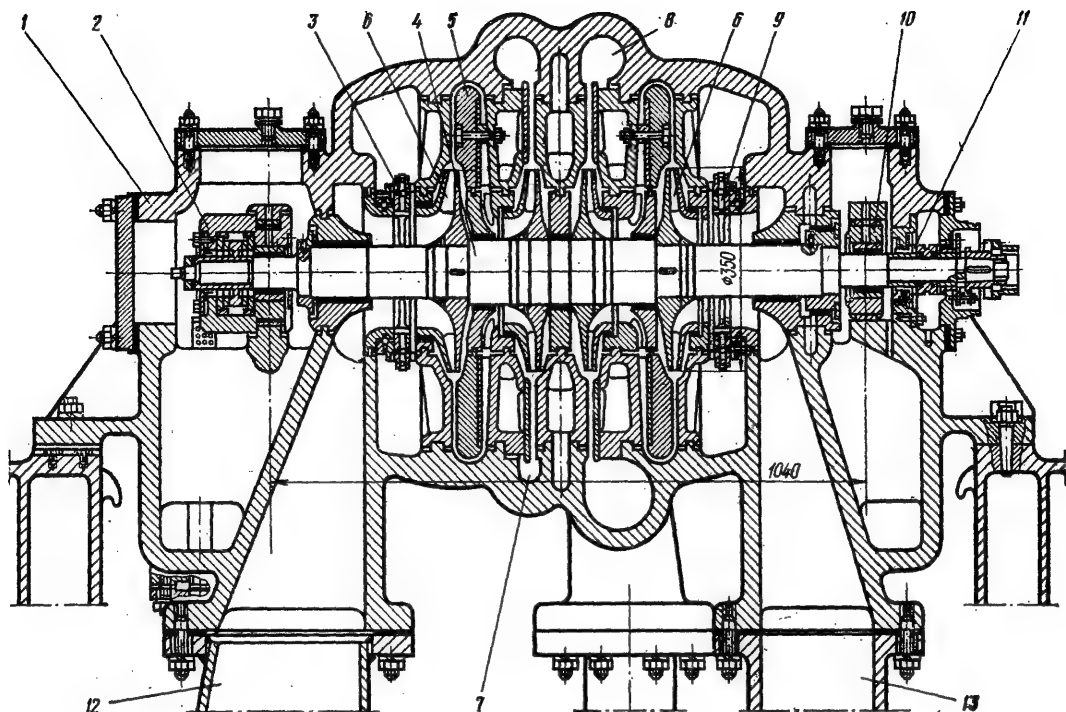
Пропановый центробежный компрессор ТКП-435:
